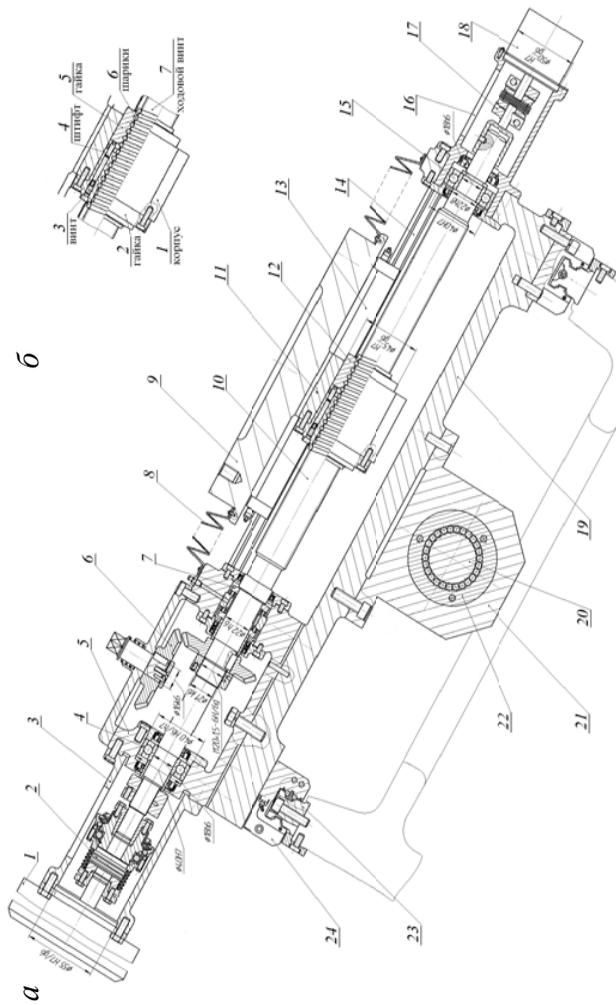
Крестовый суппорт (а) с наклонным приводом поперечной подачи каретки 9 по салазкам 19 токарного станка с ЧПУ и передачей винт-чайка качения (б):
